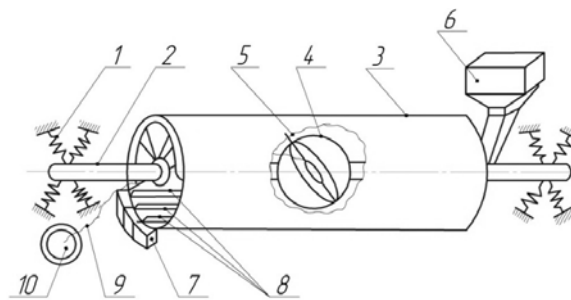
Принципова схема сепаратора з циліндричною робочою поверхнею: 1 – пружна підвіска; 2 – вісь; 3 – циліндр; 4 – віброзбудник; 5 – дебаланс; 6 – живильний пристрій; 7 – приймальники продуктів розділення; 8 – дільники; 9 – гнучкий вал; 10 – електродвигун
